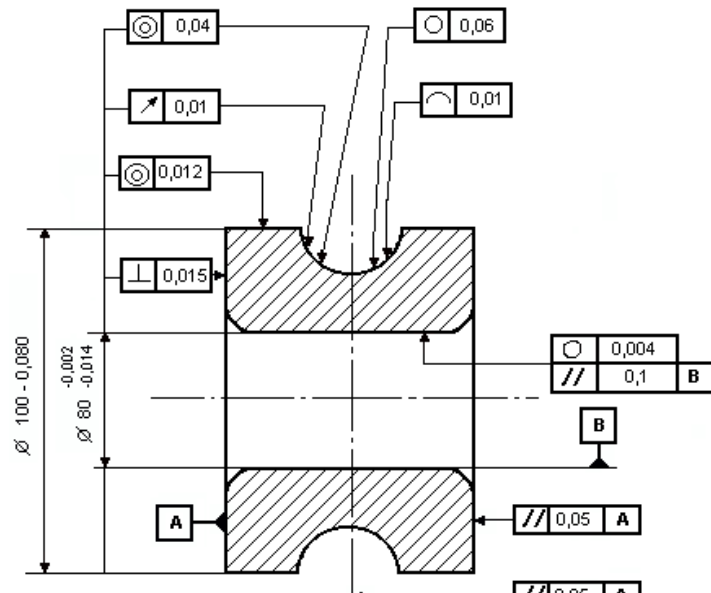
Pieza acotada con tolerancias dimensionales y geométricas
